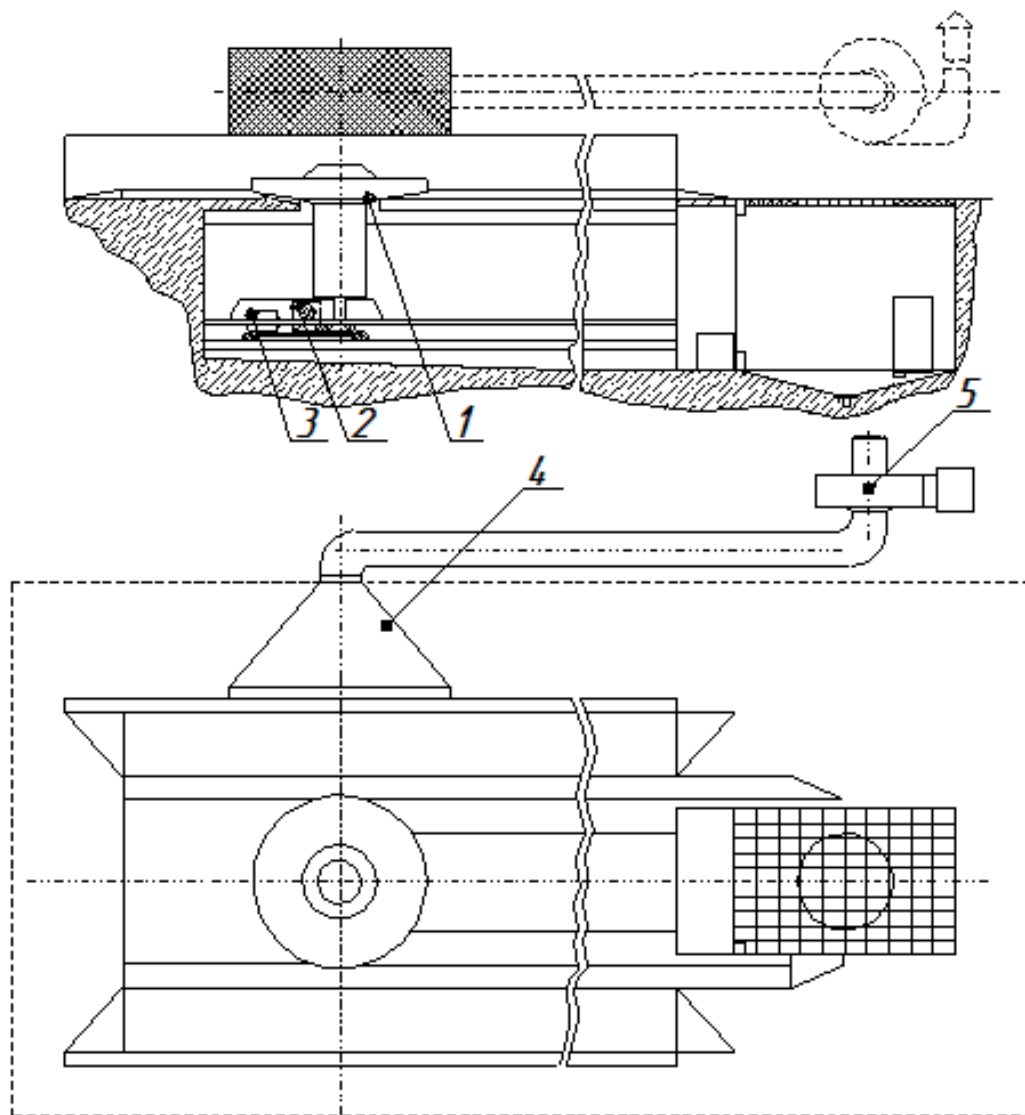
Установка для мойки днища: 1 – подвижная платформа; 2 – редуктор, 3 – электродвигатель; 4 – вытяжка; 5 – вентилятор
